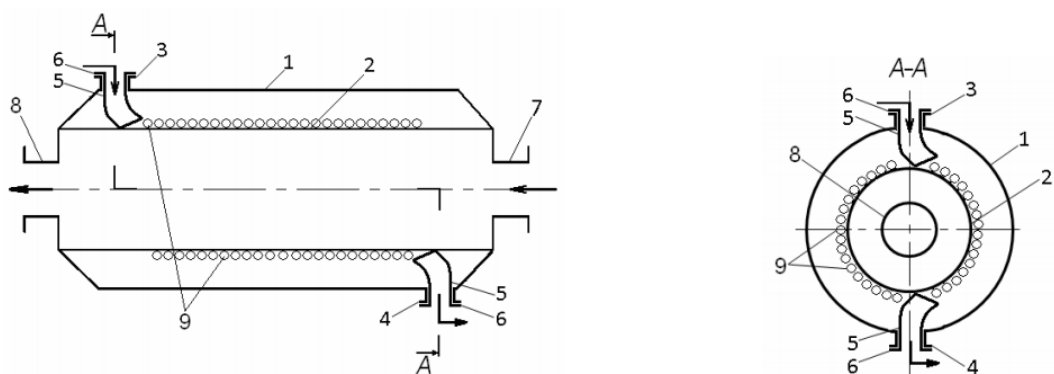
Теплообменный агрегат с устанавливаемыми в патрубки входа и выхода жидкой рабочей среды трубчатыми элементами
